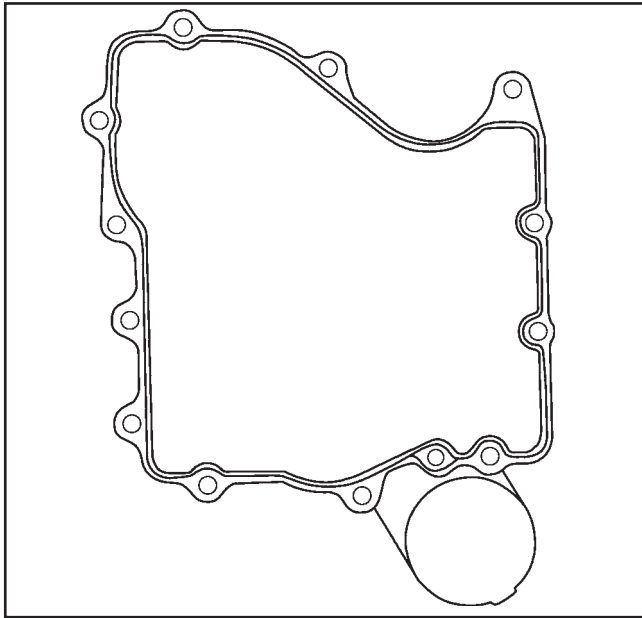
Modèle de joint sur la plaque de fermeture.
